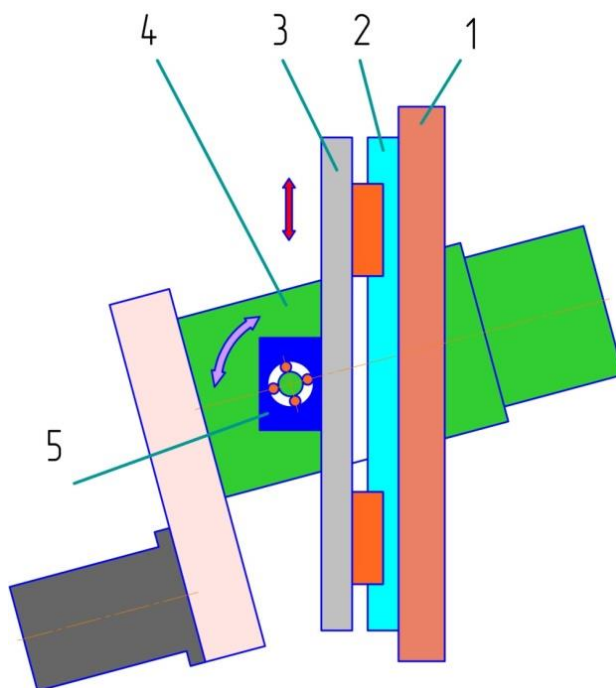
Поворотный модуль (1 – основание; 2 – направляющая; 3 – плита; 4 – корпус; 5 – корпусной подшипник)
